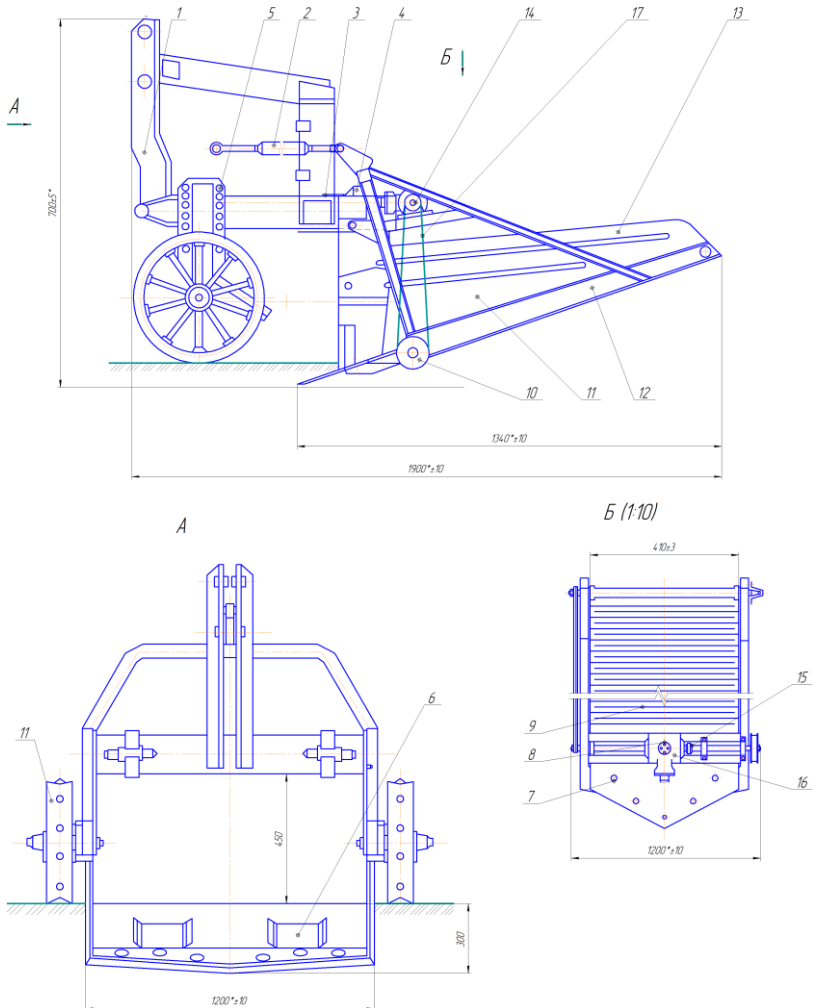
Схема розробленої скоби: 1 – начіпний механізм; 2 – тяга; 3 – карданний вал; 4 – захисний кожух; 5 – фіксатор; 6 – подовжувач; 7 – леміш; 8 – редуктор; 9 – елеватор ґрунту; 10 – ведений шків; 11 – опорне колесо; 12 – рама; 13 – захисний щит; 14 – ведучий шків; 15 – муфта втулкова; 16 – гідромотор; 17 – зубчатий пас
